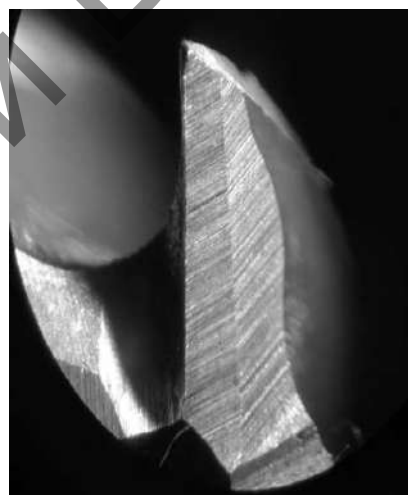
Вид стачиваемой режущей кромки зуба концевой фрезы под микроскопом
